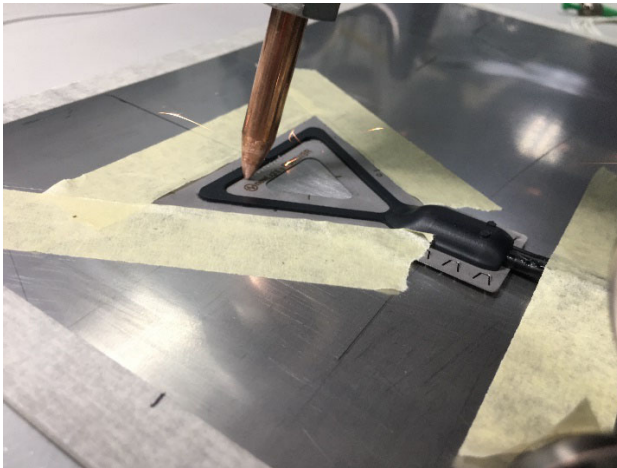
Procédure de soudage de la FS62WSR
